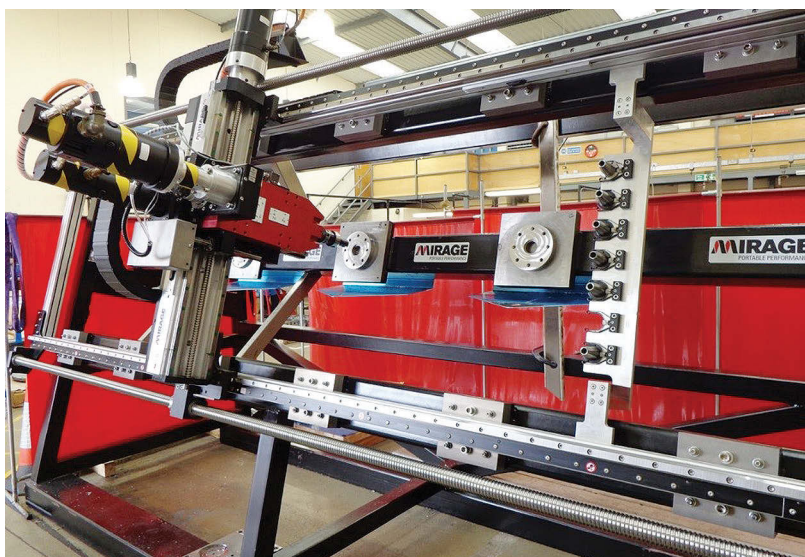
Мобильный фрезерный станок портального типа с ЧПУ
